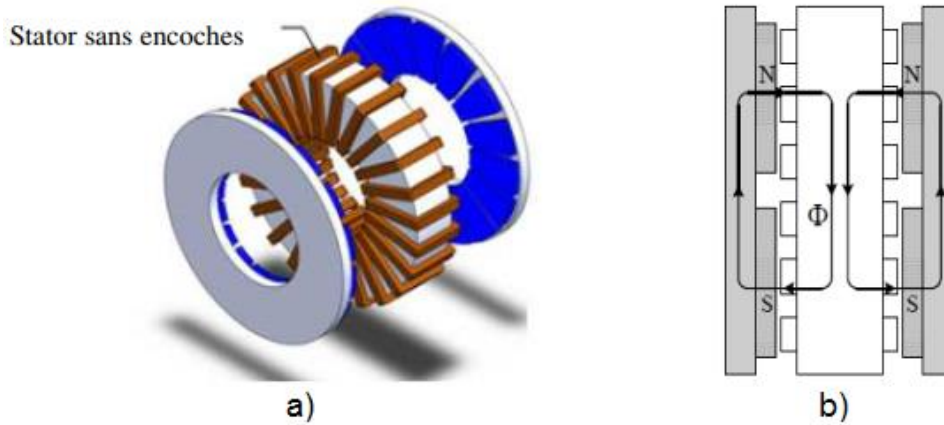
Machine à flux axial stator double rotor a) avec stator sans encoche b) type NN [23], [22]
